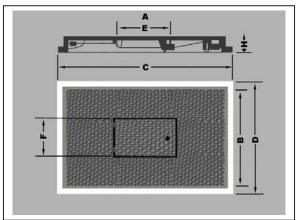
Tampa T-13 simples para instalação de hidrômetro em calçada.
